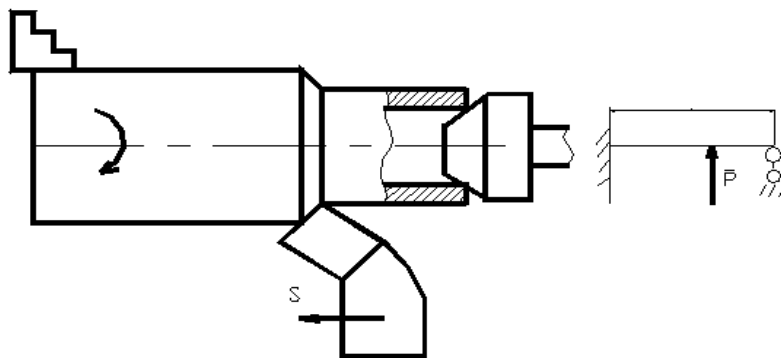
Ескіз установки заготовки та її розрахункова схема
